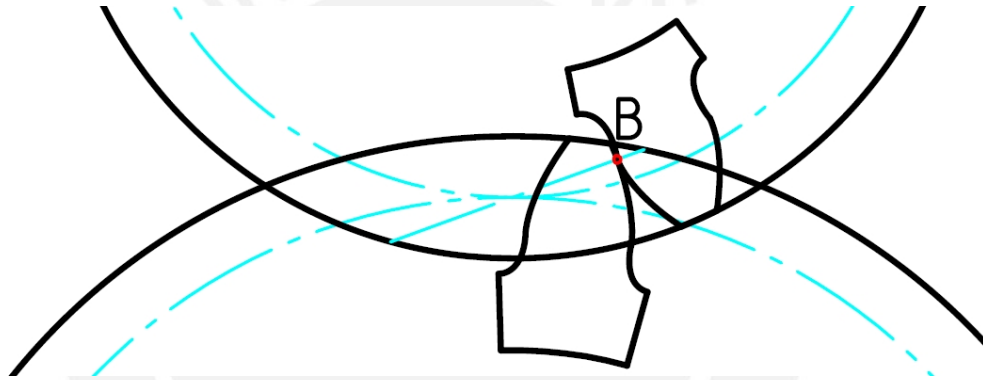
Inicio de contacto de un par de dientes – Punto B
